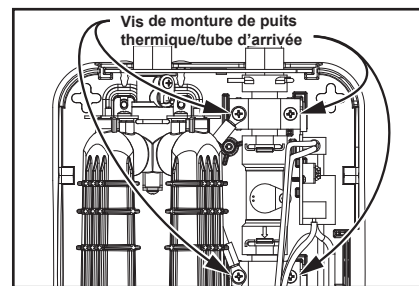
Vis de montage de puits thermique/tube d'arrivée.
